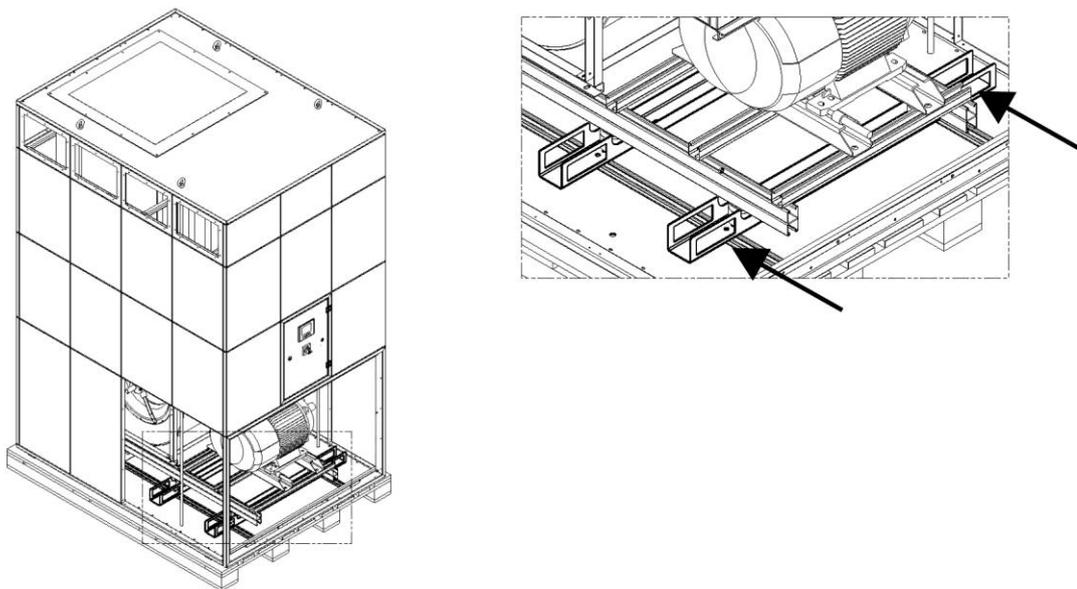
Elevación del módulo del ventilador con una carretilla elevadora
